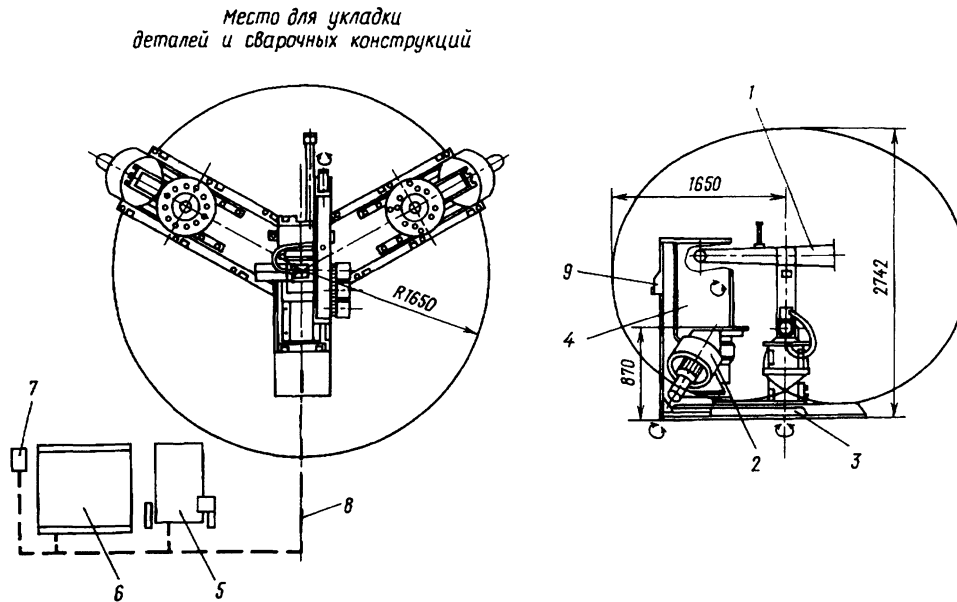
РТК для дуговой сварки типа ОЖ-10 с двумя манипуляторами изделия (Чехия):
